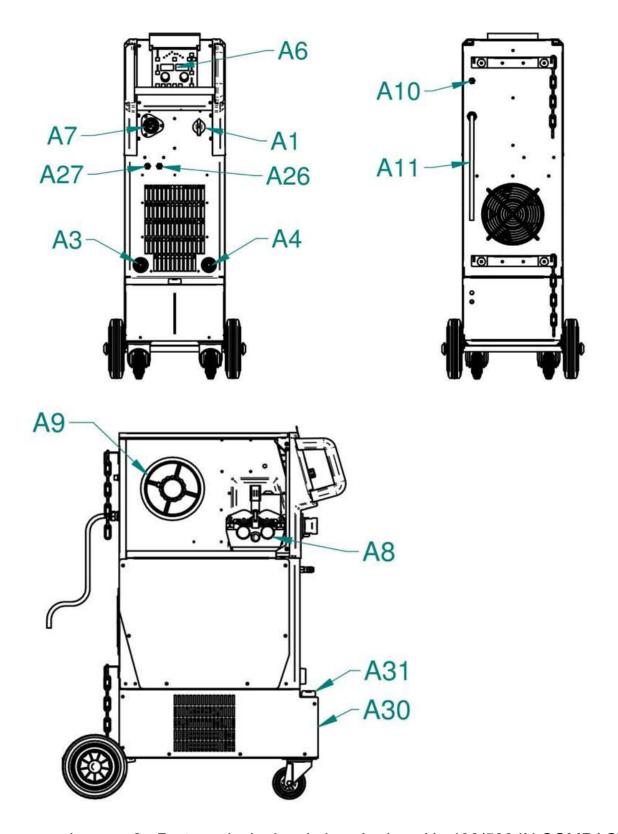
Partes principales de la máquina aXe 400/500 IN COMPACT
